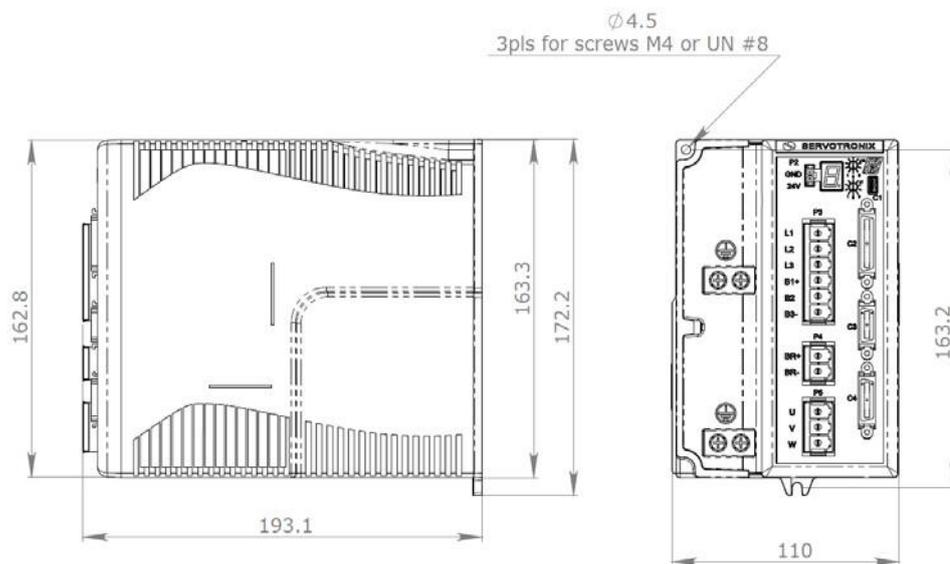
GTHD-003/GTHD-006 — 400/480 VAC —外形尺寸 (mm)
